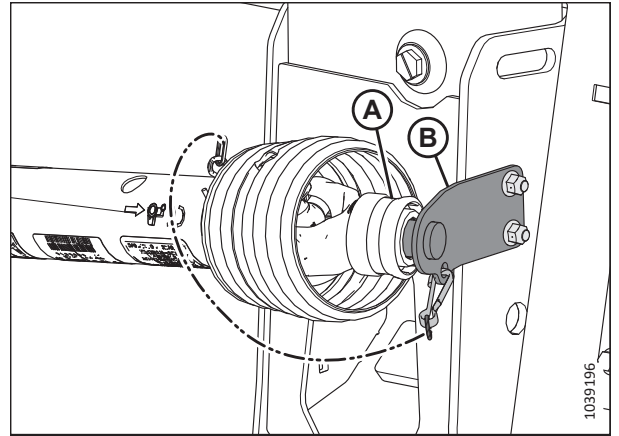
Приводний вал у положенні для зберігання — приводний вал B7038 або B7039
